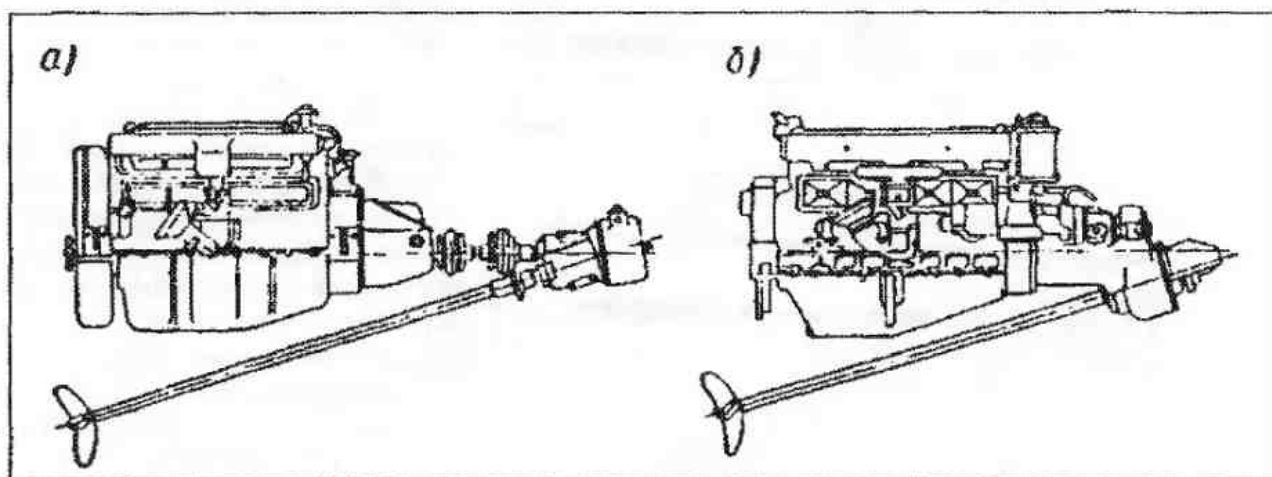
Два вида углового редуктора для стационарного двигателя:
